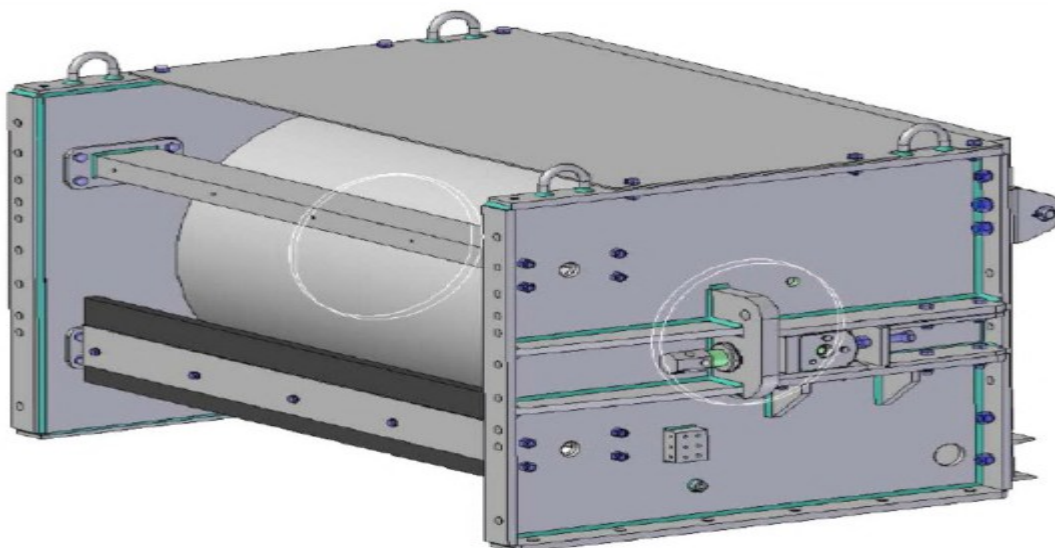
Hnací buben s pásy keramiky Flex-Lag Weld-On od firmy DvB-AF s.r.o. [9]
